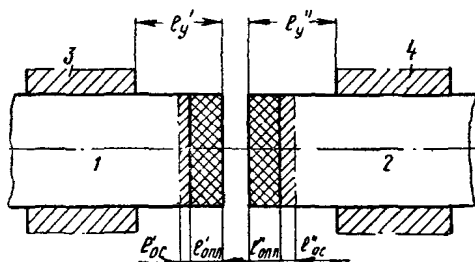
Геометрические параметры режима стыковой сварки стержней
